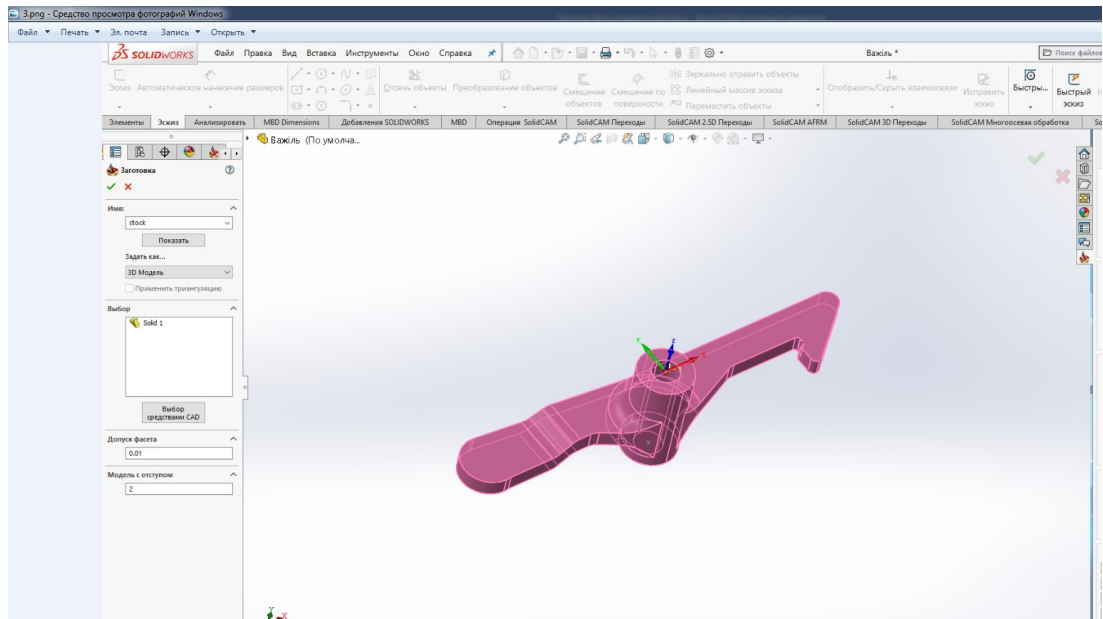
Заготовка завантажена в SolidCAM
